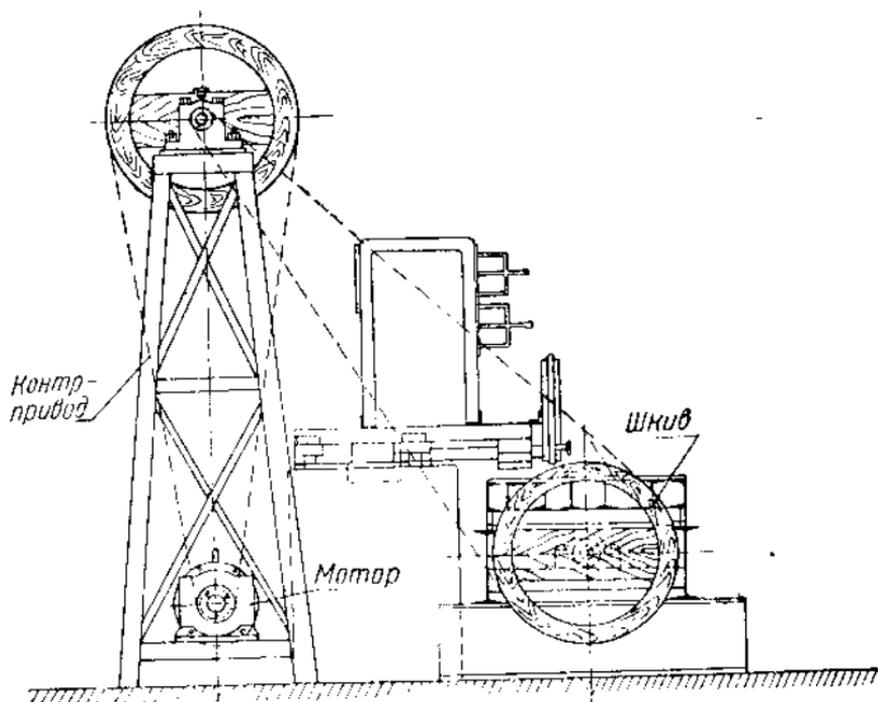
Фрезерный станок с автоматической подачей (вид сбоку)
